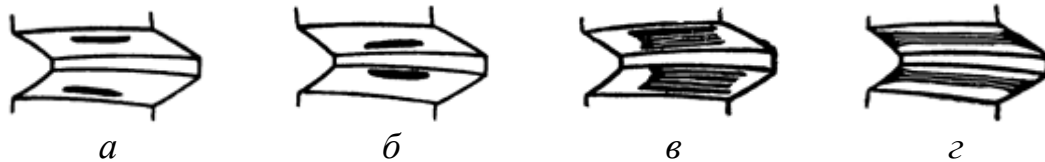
Типові види похибок розміщення плями контакту на зубцях конічних зубчастих коліс: при вершині зуба (а); близько до ніжки зуба (б); з розривом по висоті зуба (в); з розривом по довжині зуба (г)
